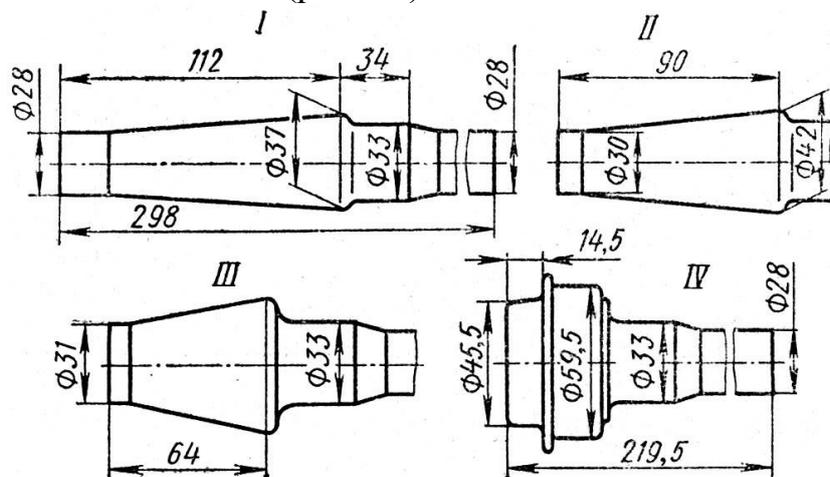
Набор металла (I-III) и высадка головки заготовки детали (IV)
